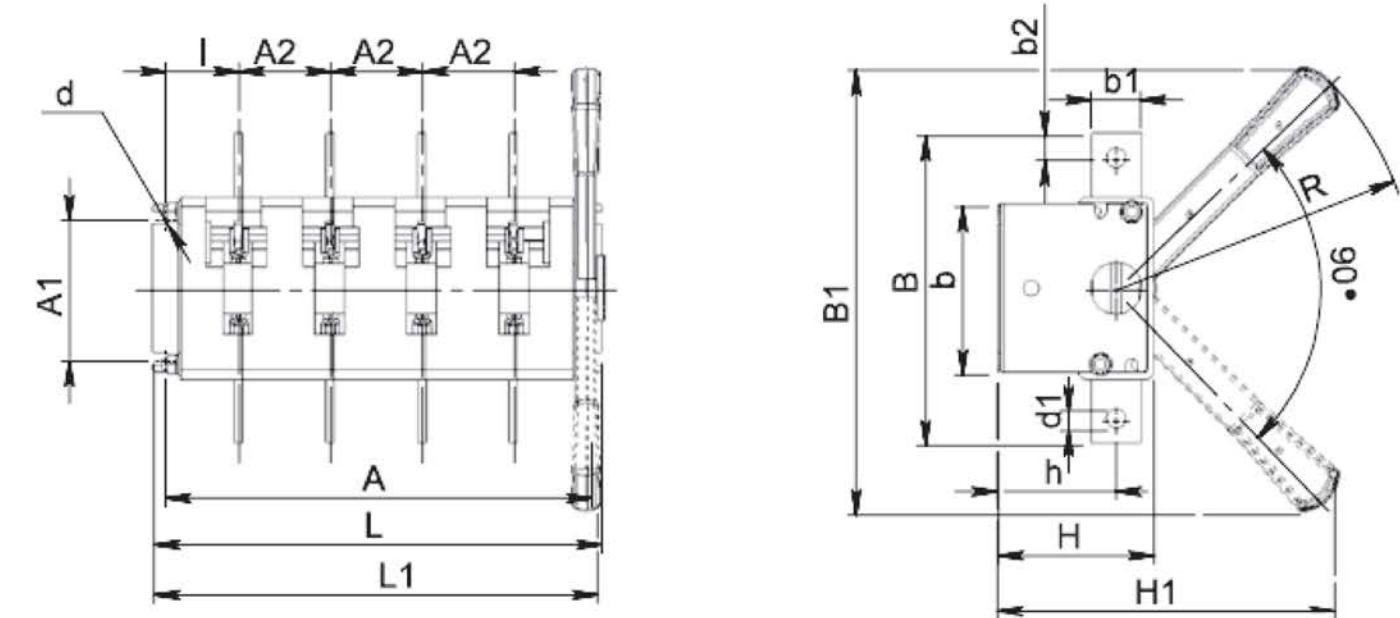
Выключатель-разъединитель четырехполюсный на одно направление с боковой смещенной рукояткой.
